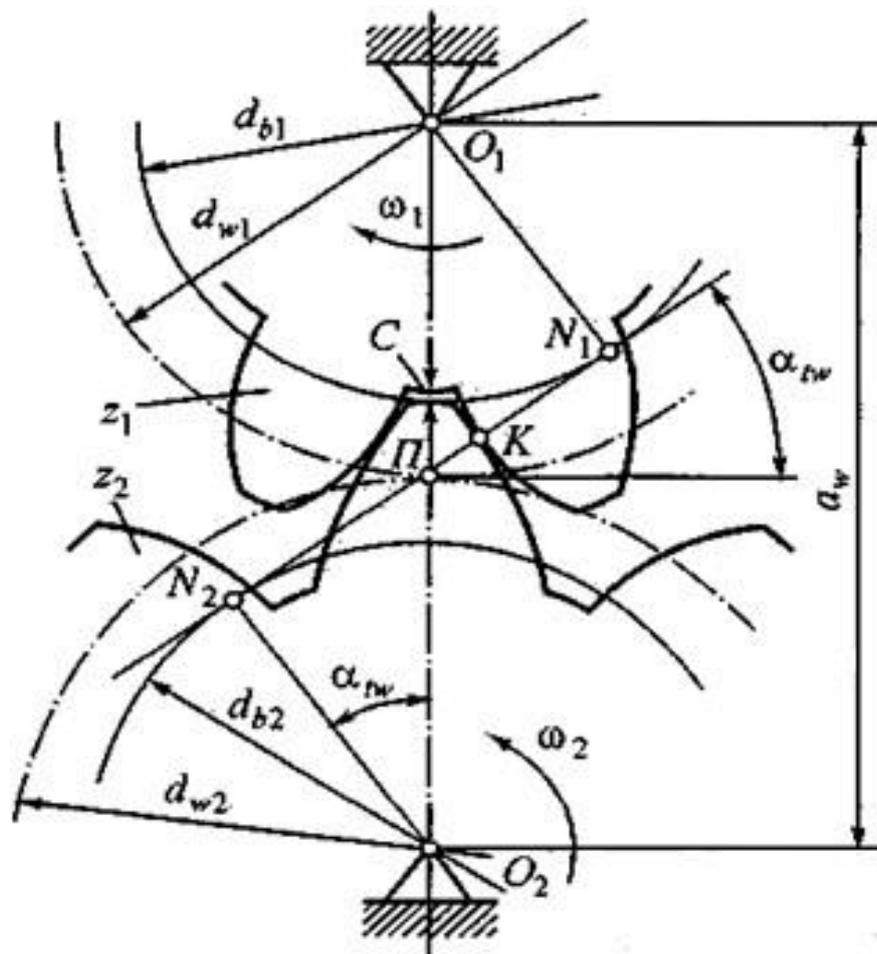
Зацепление эвольвентных зубчатых колес
